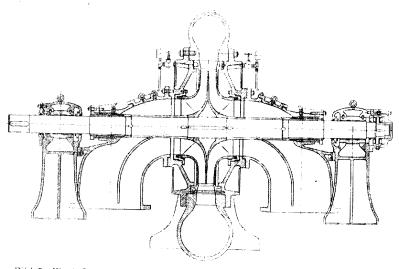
Einstufige Spiralgehäusepumpe mit Leitrad und zweiseitigem Einlauf
